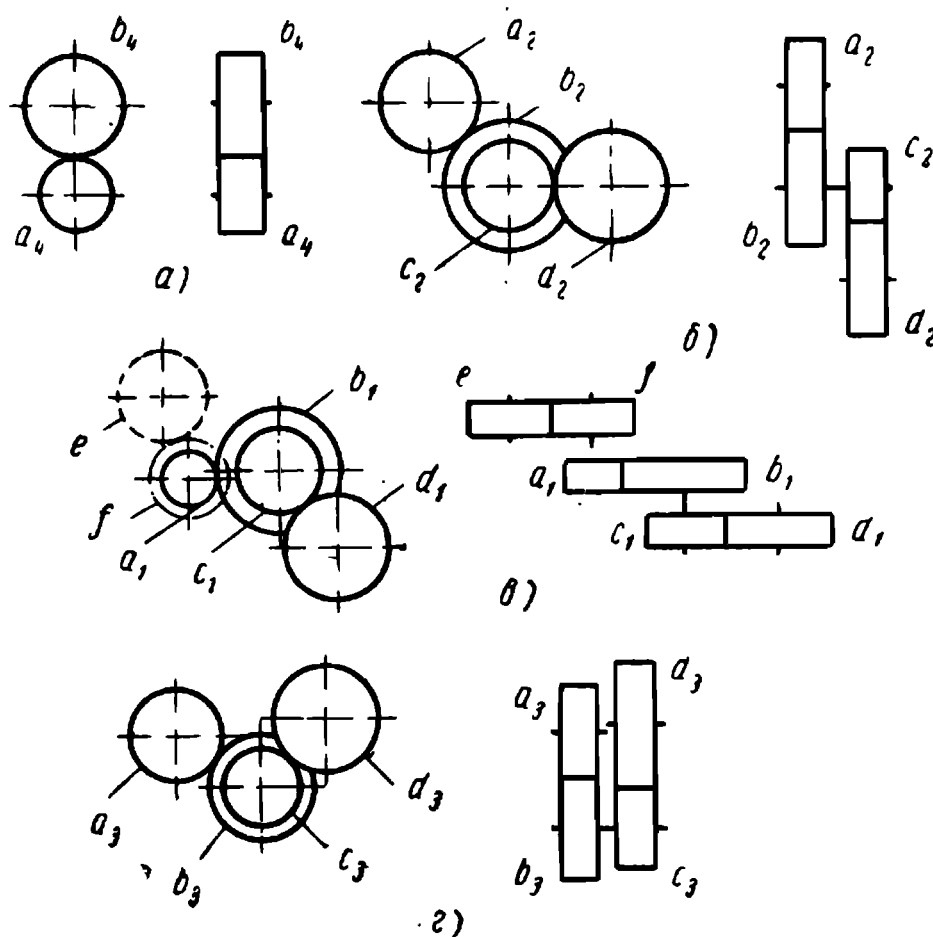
Эскизы гитар зубофрезерного станка 5Д32 с указанием размещения сменных колес:
